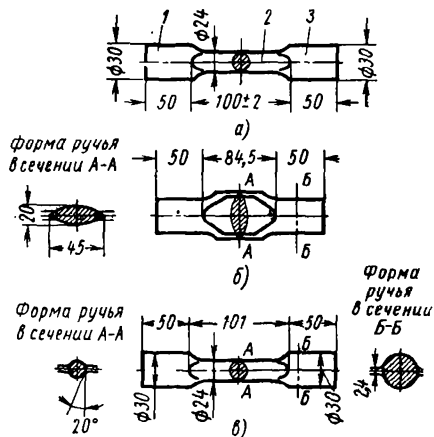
Фасонная заготовка шатуна: а — чертеж заготовки; б и в — заготовка после первого и второго проходов в вальцах
